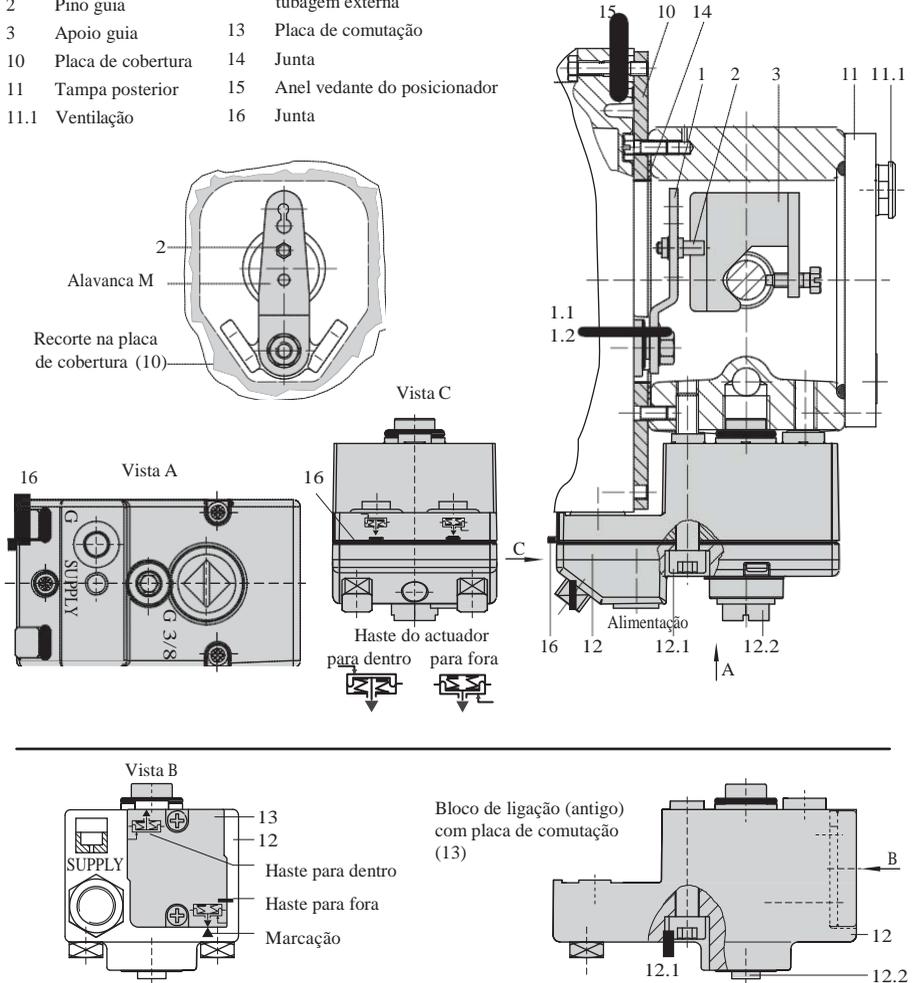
Montagem directa – Ligação do sinal pneumático para o actuador Tipo 3277 com 240, 350, 355 e 700 cm²
